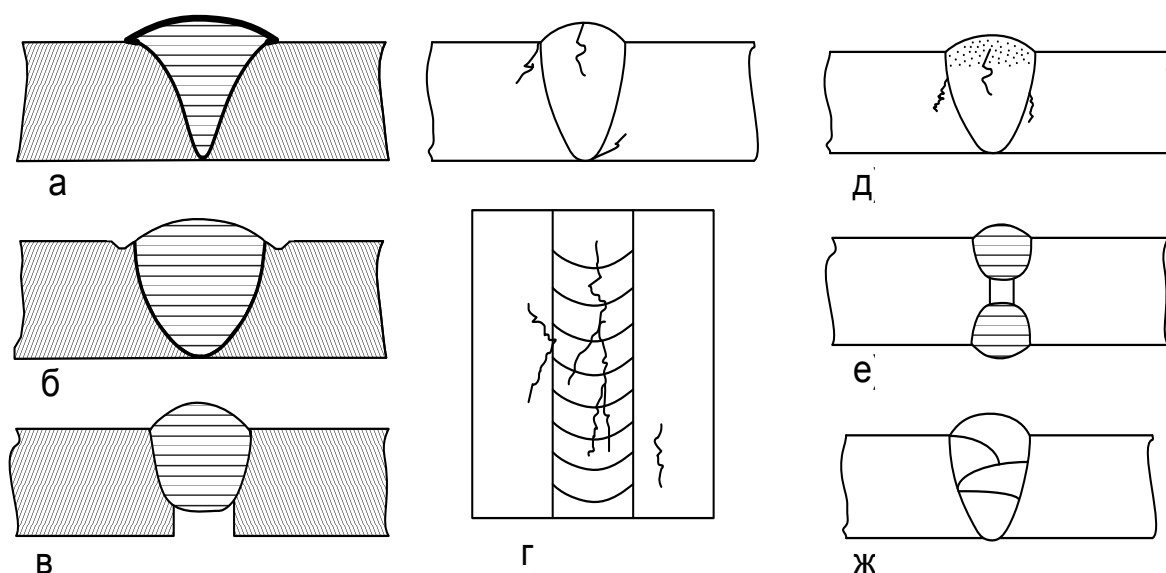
Виды дефектов сварных соединений:
